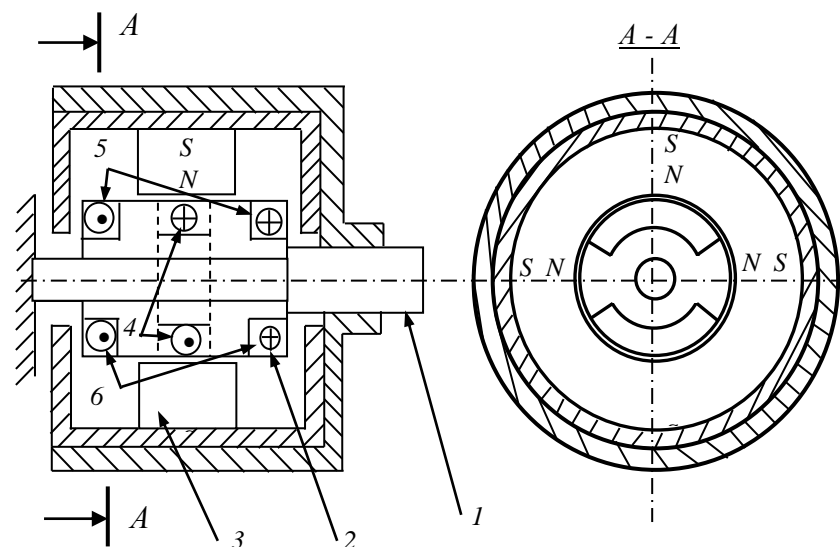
Конструкция магнитного подшипника: 1 – вал; 2 – статор; 3 – постоянный магнит; 4 – кольцевая обмотка; 5, 6 – сегментные обмотки
